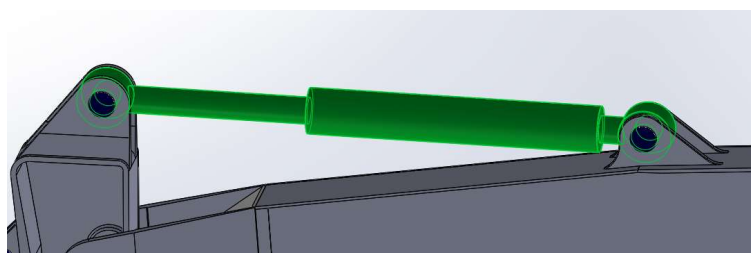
Ensamblajes unidos rígidamente (II)
